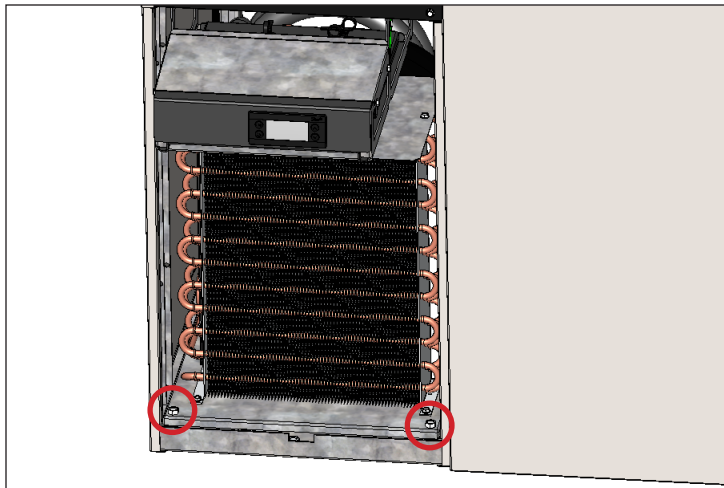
Die Schrauben des Verflüssigersockels entfernen.
